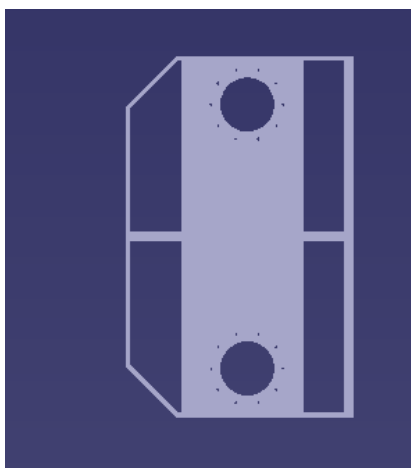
Vista detallada de la cadera, anterior a la modificación.
